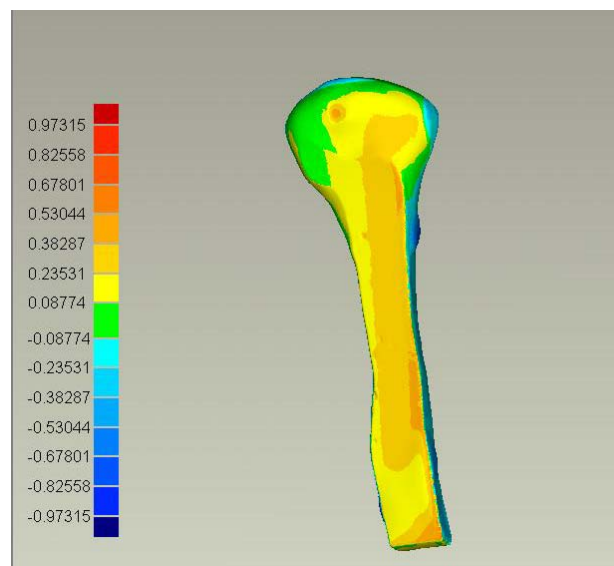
Comparação dimensional do modelo físico produzido por usinagem CNC e do modelo virtual projetado em CAD.
